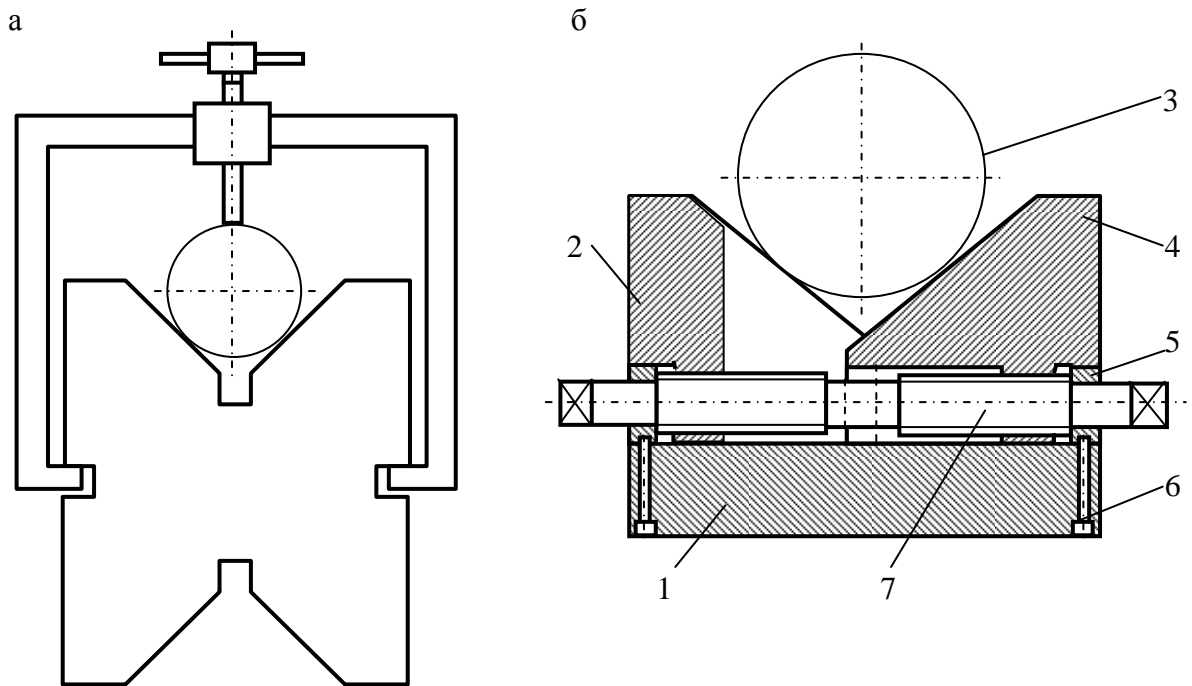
Типи призми: а-жорстка; б- регульована; 1-основа; 2,4-щока; 3-виріб; 5-опора; 6-гвинт стопорний; 7-гвинт регульовальний.
